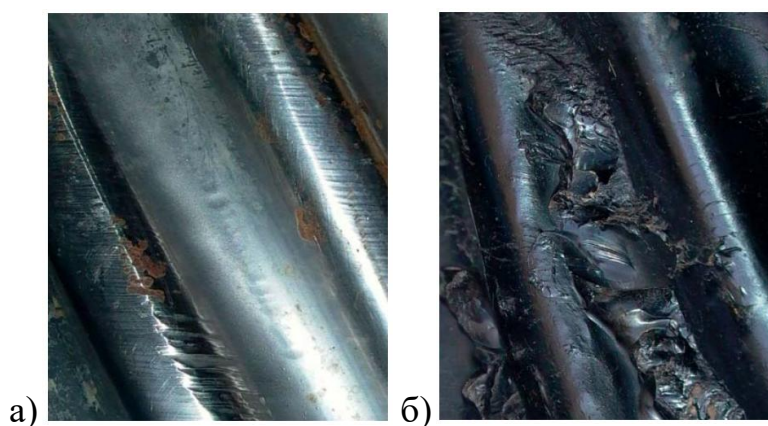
Износ поверхностей рабочей пары: а) ротора; б) обкладки статора
